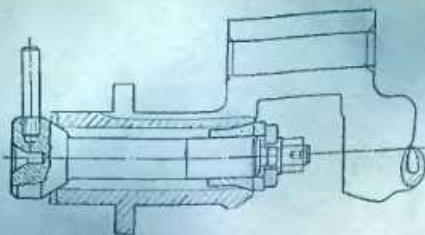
Центрирующая пробка для установки вала на шлифовальном станке
